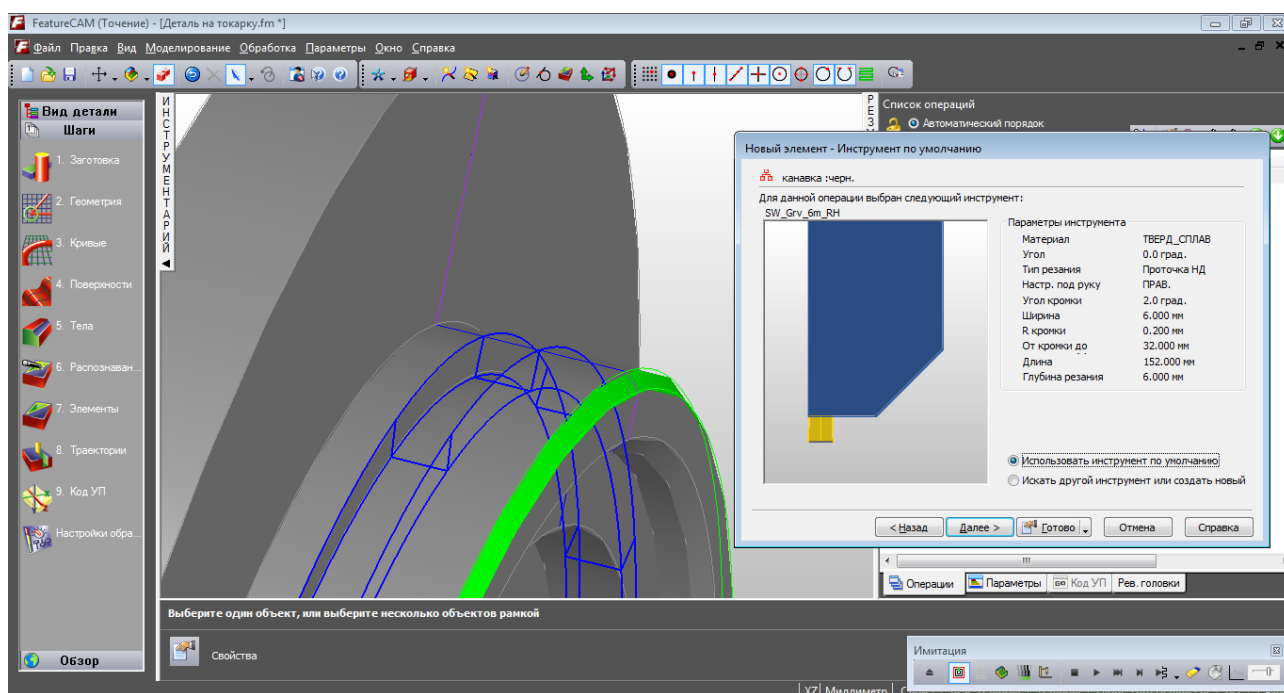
Вибір інструменту для прорізання канавки
